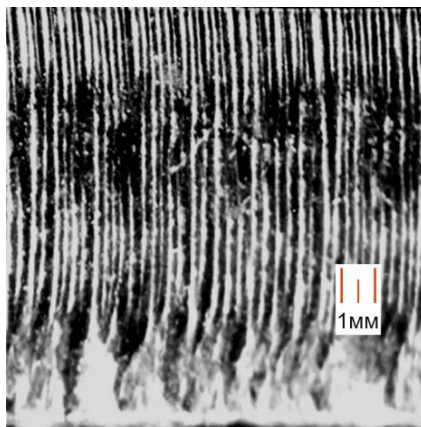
Вигляд поверхні різку після лазерного різання сталі 45
